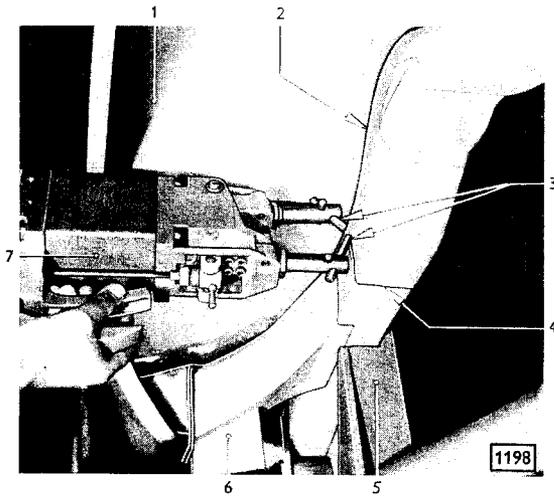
Vom Radeinbau aus zugänglichen äußeren Flansch des Längsträgerhinterteiles punktschweißen
